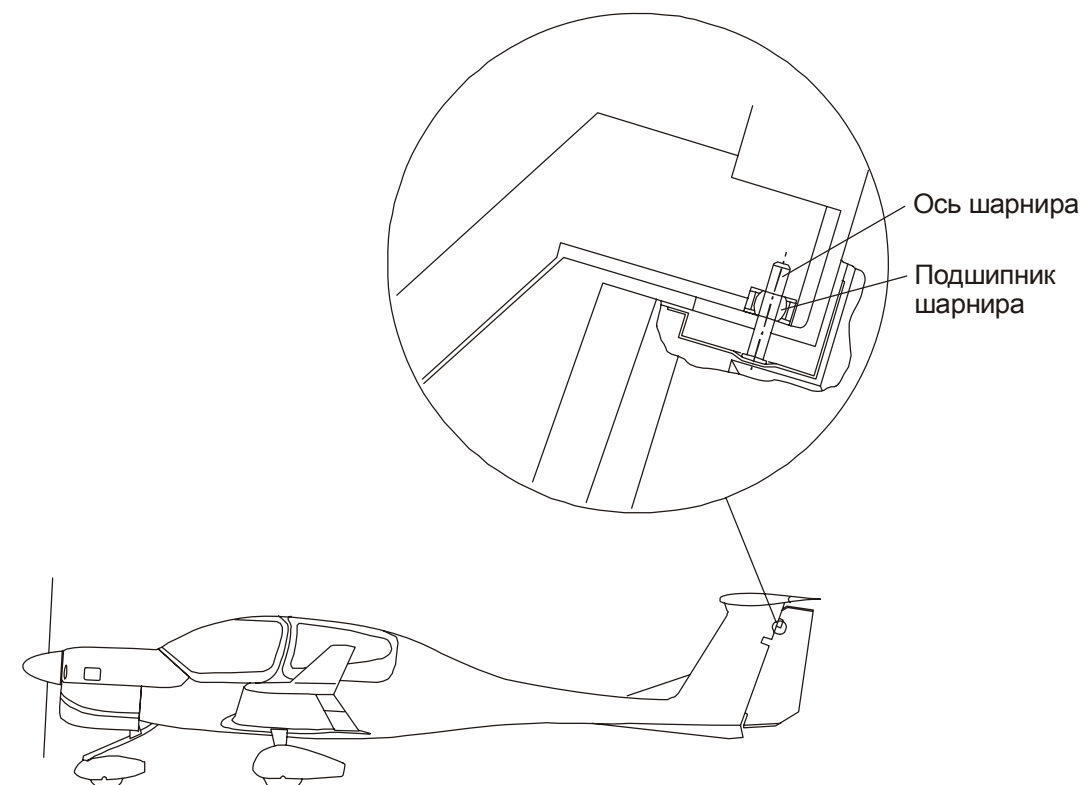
Втулка для обеспечения зазора между рулем направления и шарнирной опорой руля направления
